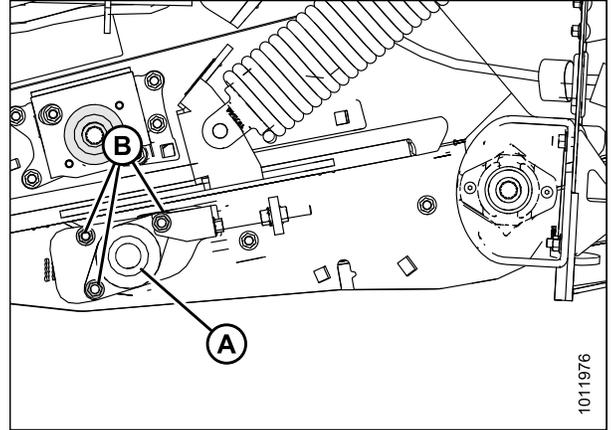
Rodillo tensor de la cama frontal del lado izquierdo
